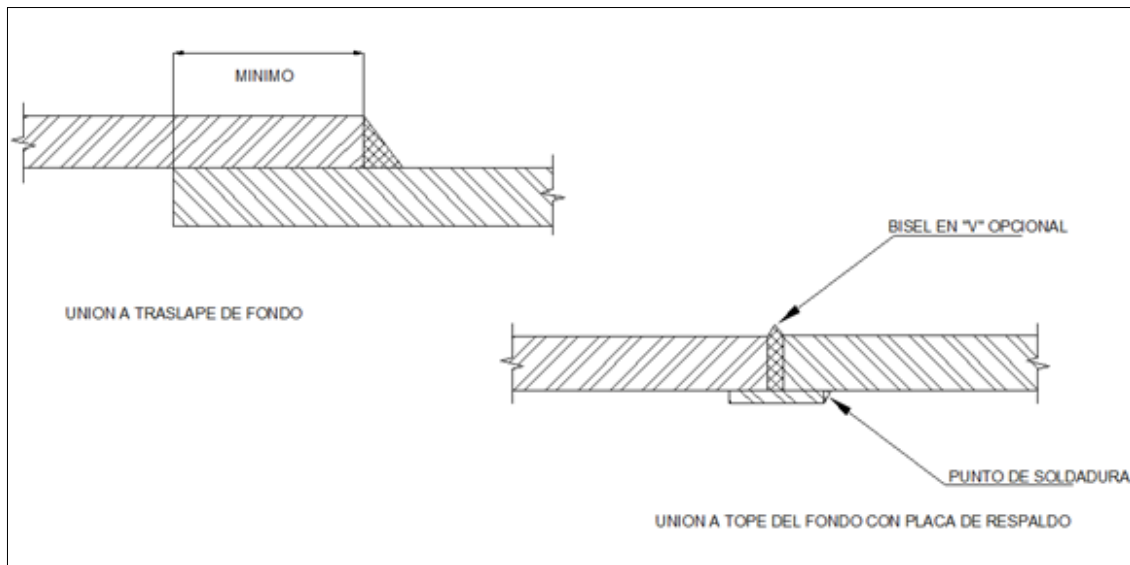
Detalles Típicos de Soldaduras del Fondo.
